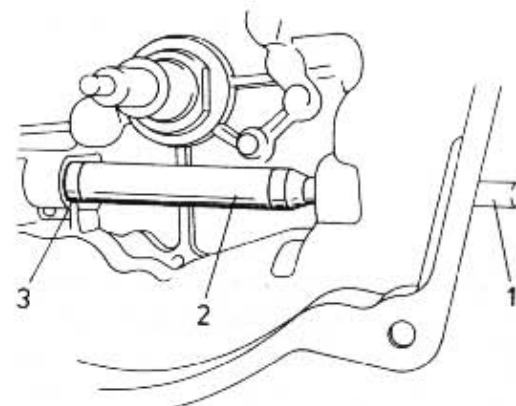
WKREĆCENIE GWINTOWNIKA W ZEWNĘTRZNA TULEJKĘ ŁOŻYSKUJĄCĄ WAŁEK WYŁĄCZAJĄCY SPRZĘGŁO
